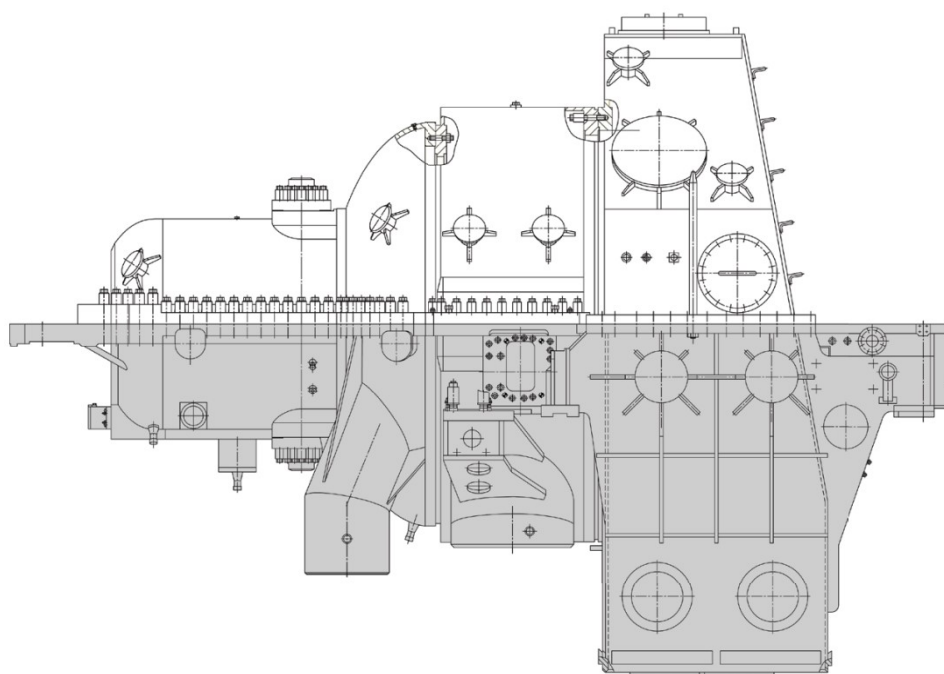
Цилиндр в сборе турбины Т-63/76-8,8
